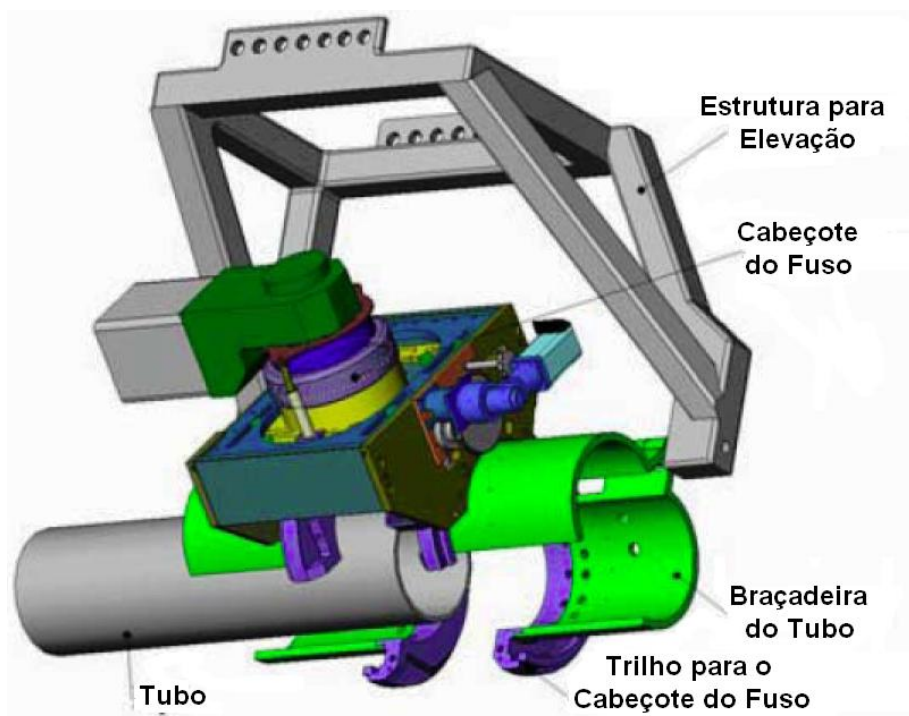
Equipamento para execução de soldagem circunferencial de tubos pelo processo de fricção linear [Feng 2005].
